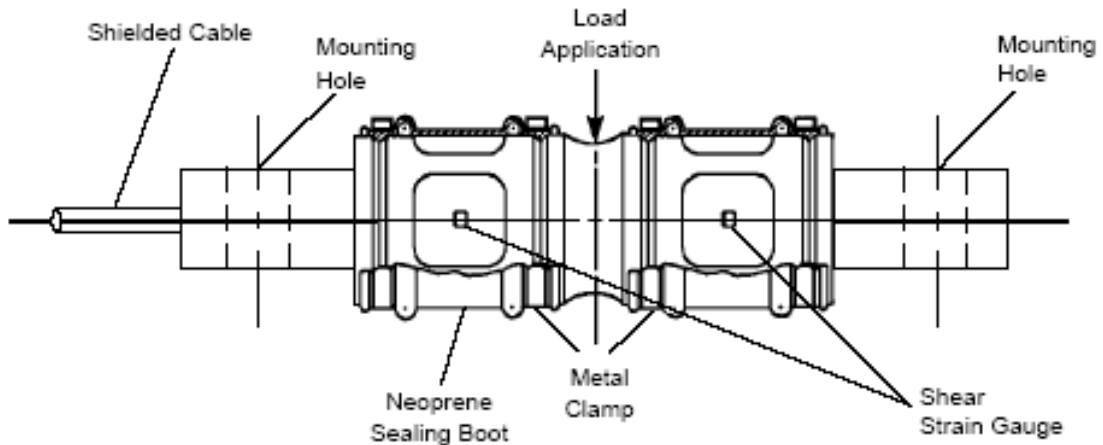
Celda de carga tipo viga con dos punto de apoyo
